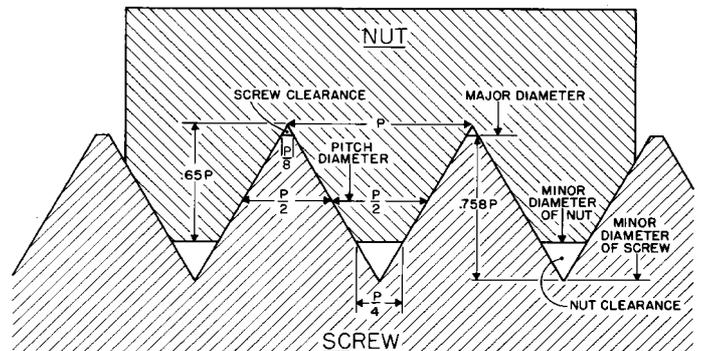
Die verschiedenen Teile eines Gewindes, das mit einem 60° Gewindestahl geschnitten wurde
